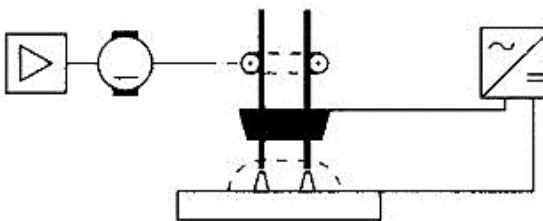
UP-Doppeldraht- oder Parallelschweißen (schematisch) [7]
